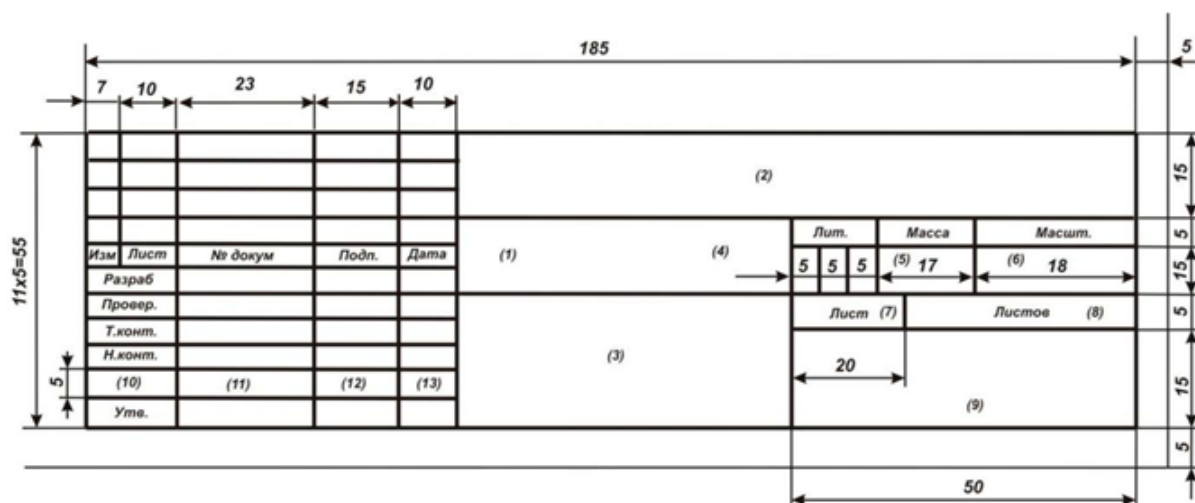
Основная надпись для чертежей и схем, форма 1
